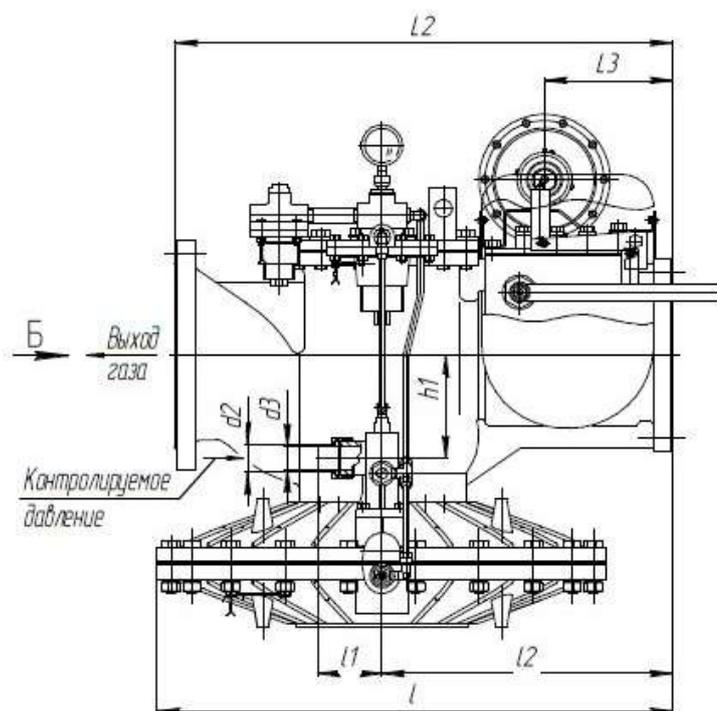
Общий вид и габаритные размеры регуляторов РДГ-Н
